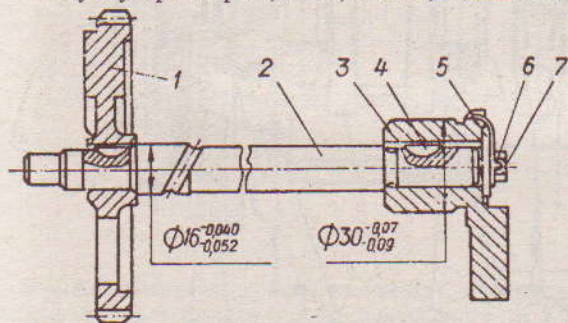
Механизм балансирующий в сборе: 1 - шестерня балансирующего вала; 2 - вал балансирующий; 3 - противовес; 4 - шпонка сегментная; 5 - шайба балансирующего вала; 6 - шайба стопорная; 7 - болт М6х16
